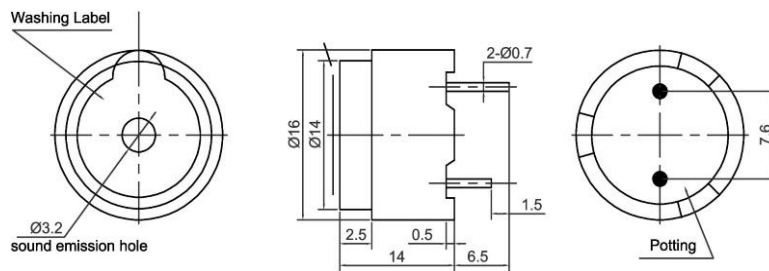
Зовнішній вигляд зумера HCM1606X
